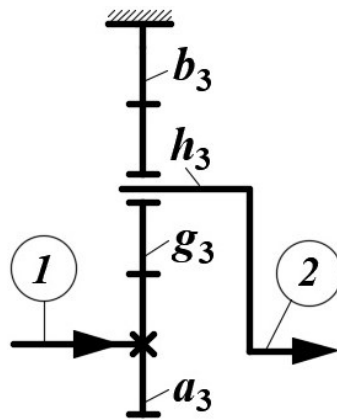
Трехзвенный планетарный механизм с одновенцовыми сателлитами
